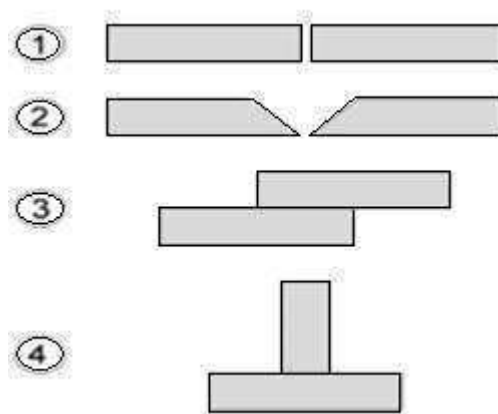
Tipos comunes de juntas de soldadura: (1) La juntura de extremo cuadrado, (2) Juntura de preparación solo-V, (3) Juntura de regazo o traslape, (4) Juntura-T.
